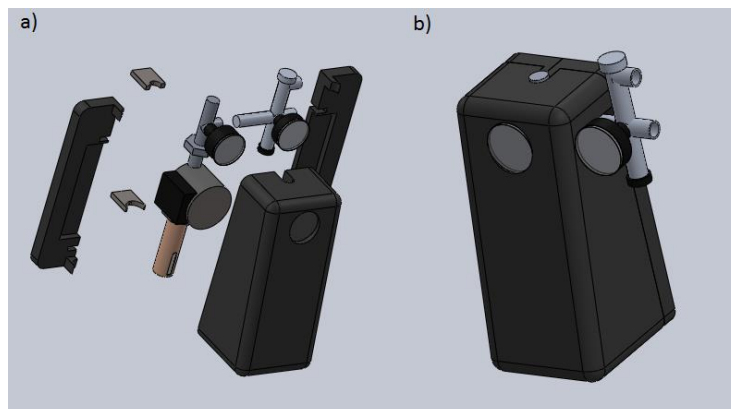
Desenho tridimensional do grupo hidráulico solar hydraulic 10 simples com: a) vista explodida e b) conjunto final.
